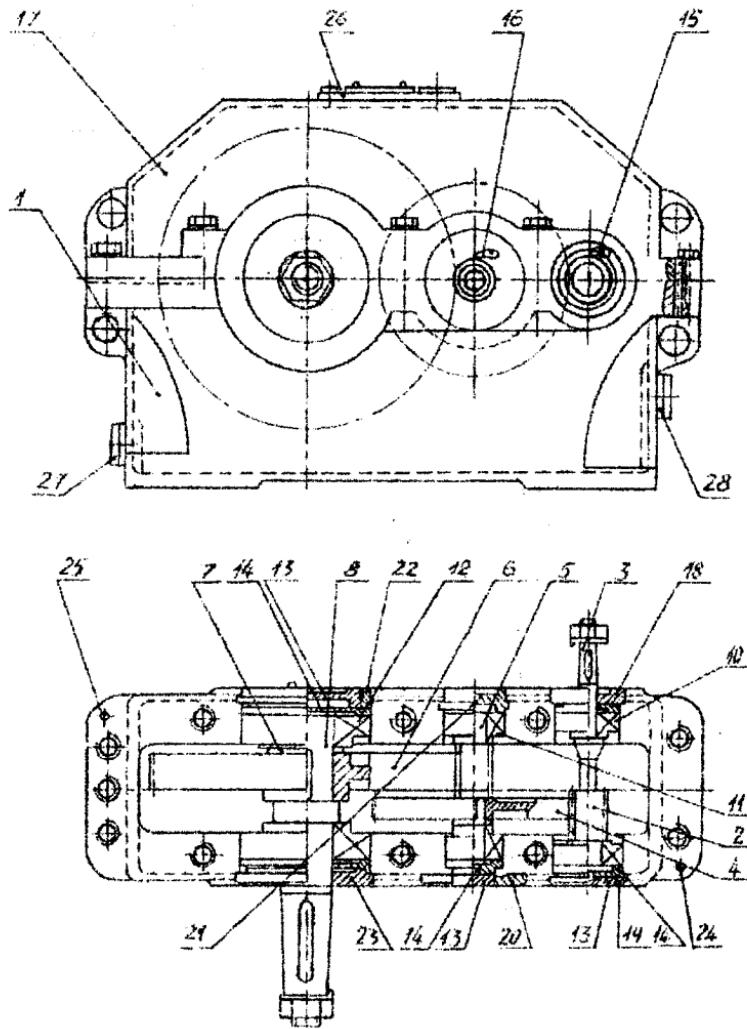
Конструкція двоступінчастого редуктора Ц2У-160
